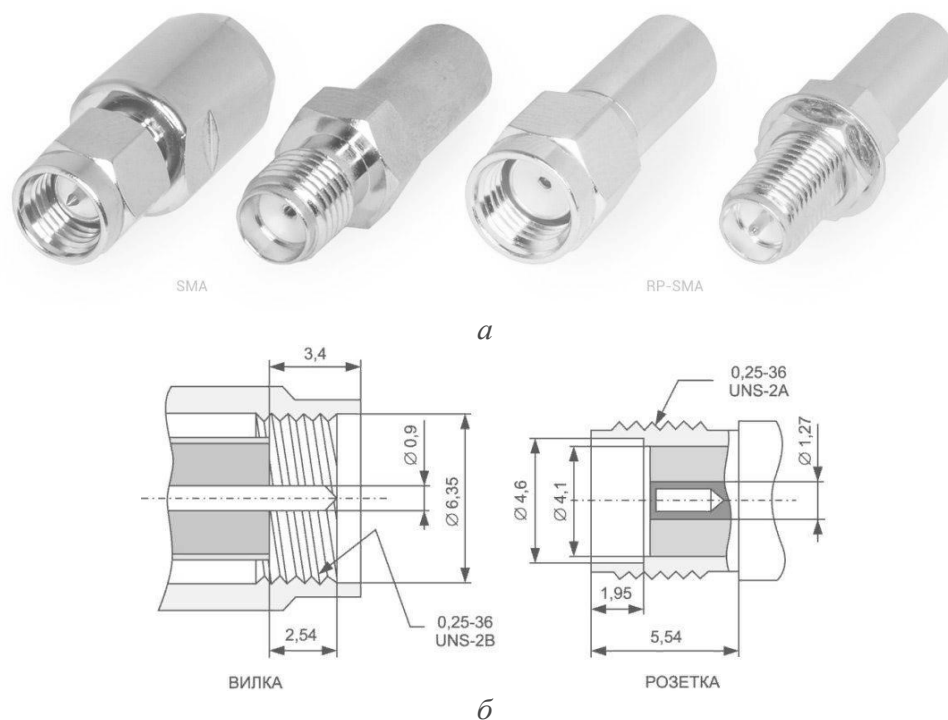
Соединитель SMA: *a* — внешний вид; *б* — габаритные размеры.
